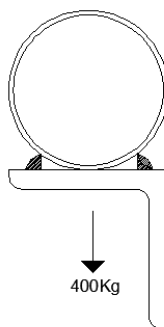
(Esquema de la soldadura superior del pórtico)
